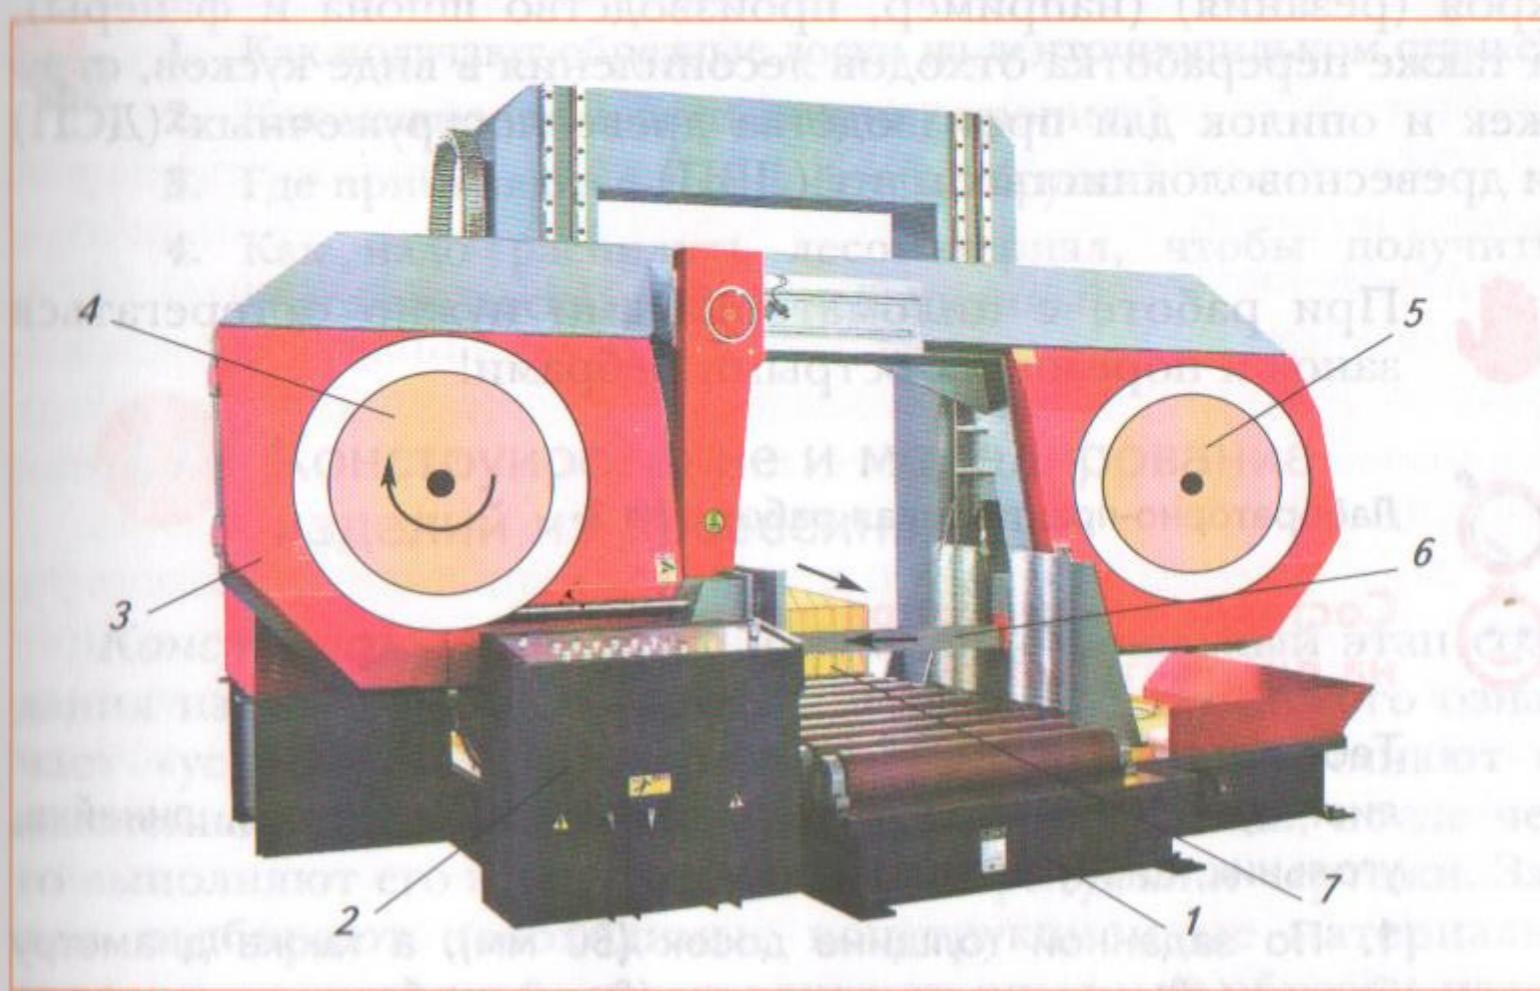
Ленточнопильный станок: 1 — стол с вальцами для подачи материала; 2 — пульт управления; 3 — суппорт; 4 — приводной шкив; 5 — неприводной шкив; 6 — ленточная пила; 7 — распиливаемый брус
